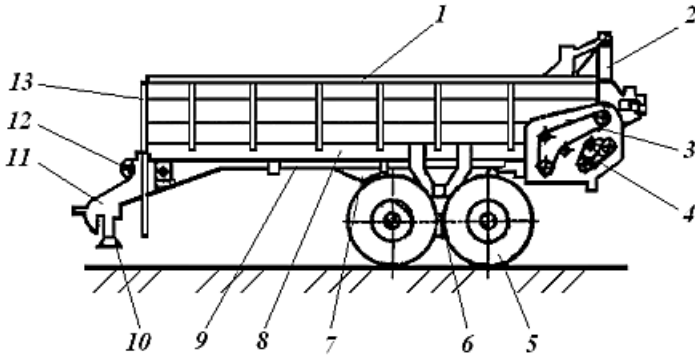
Причіп-розкидач органічних добрив ПРТ-10: 1 - кузов; 2 - розкидач; 3 - привод розкидача; 4 - привод транспортера. 5 - ходова система; 6 - балансир; 7 - трос, 8 - рама; 9 - трансмісія; 10 - опора; 11 - дишло; 12 - карданна передача; 13 - драбинка.
